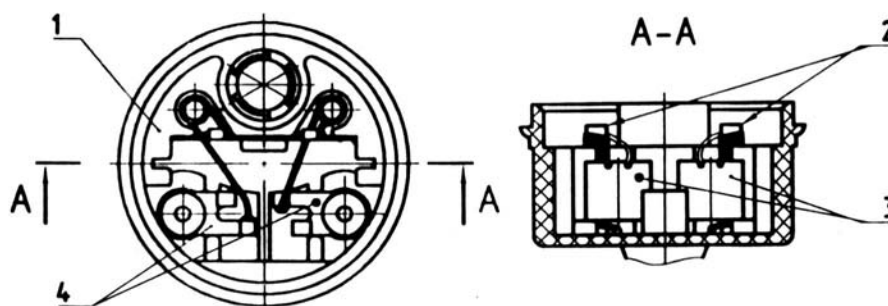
Расположение контактной группы выходной крышки ЭБН: 1 – корпус выходной крышки; 2 – индукционный фильтр; 3 – щеточный контакт; контактная пластина
